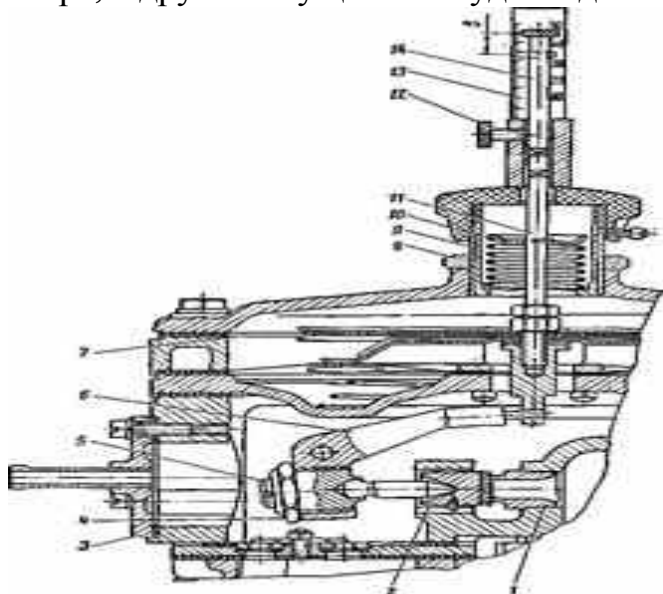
Приспособление для замера хода клапана второй ступени редуктора МКЗ-НАМИ:
